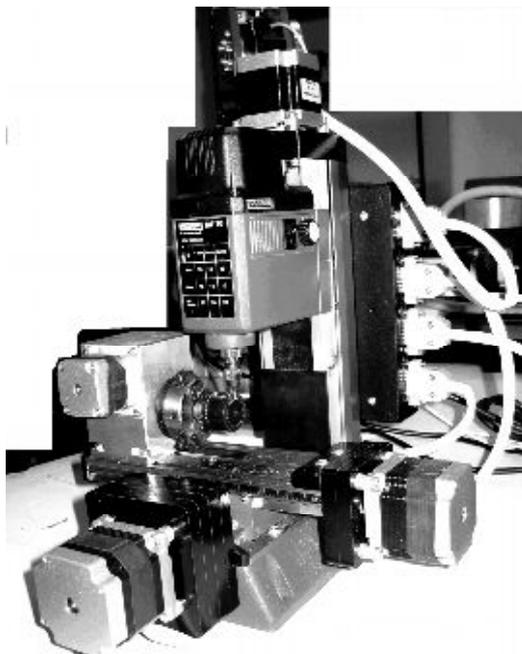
Учебный фрезерный станок с компьютерной системой ЧПУ и четырьмя управляемыми координатами
